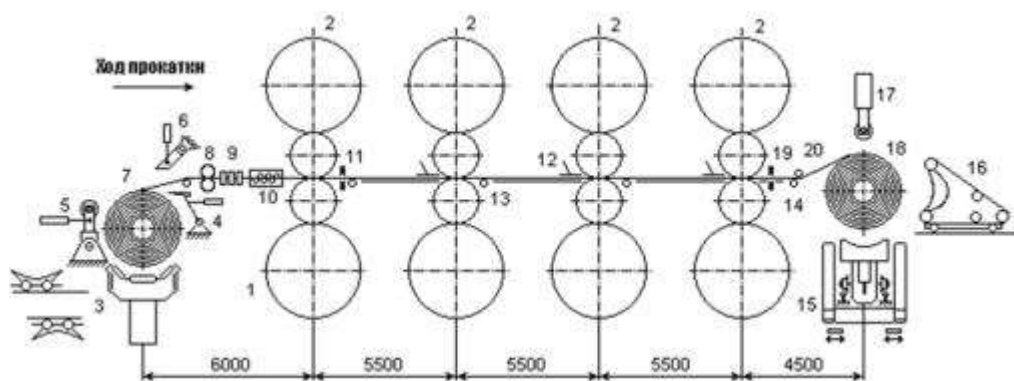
Схема расположения основного оборудования стана 2500: 1–4–х клетевой стан 2500; 2– клеть «кварто»; 3– загрузочный конвейер и роликовый подъемный стол; 4–скребок отгибателя полосы; 5– ролик прижимной; 6– прижим полосы; 7– барабан разматывателя с рулоном; 8– ролики задающие; 9– ролики центрирующие вертикальные; 10– пресспроводка; 11– изотопный измеритель толщины полосы; 12– проводковый стол; 13, 14 – ролик тензометрический; 15– тележка, кантователь; 16– захлестыватель; 17– ролик прижимной; 18– барабан моталки с рулоном; 19– изотопный измеритель толщины полосы; 20– ролик обводной
